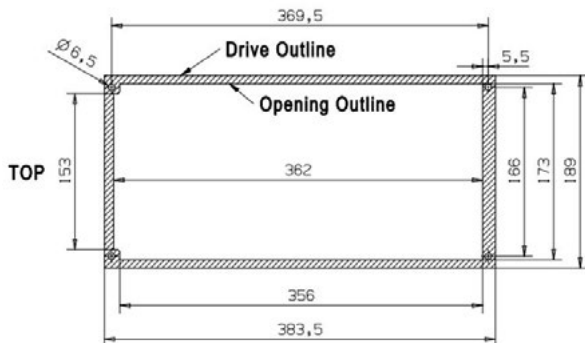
Dimensões do recorte para montagem com flange do MR4 (unidade: mm)
